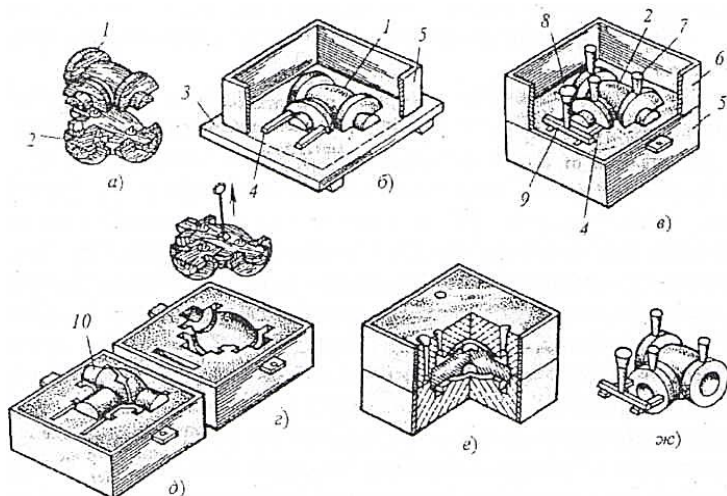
Последовательность операций изготовления литейной формы для корпуса вентиля
